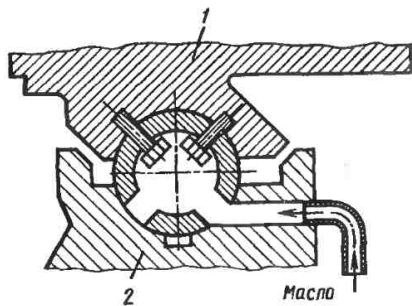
Гидростатическая смазка направляющих фрезерального станка:
